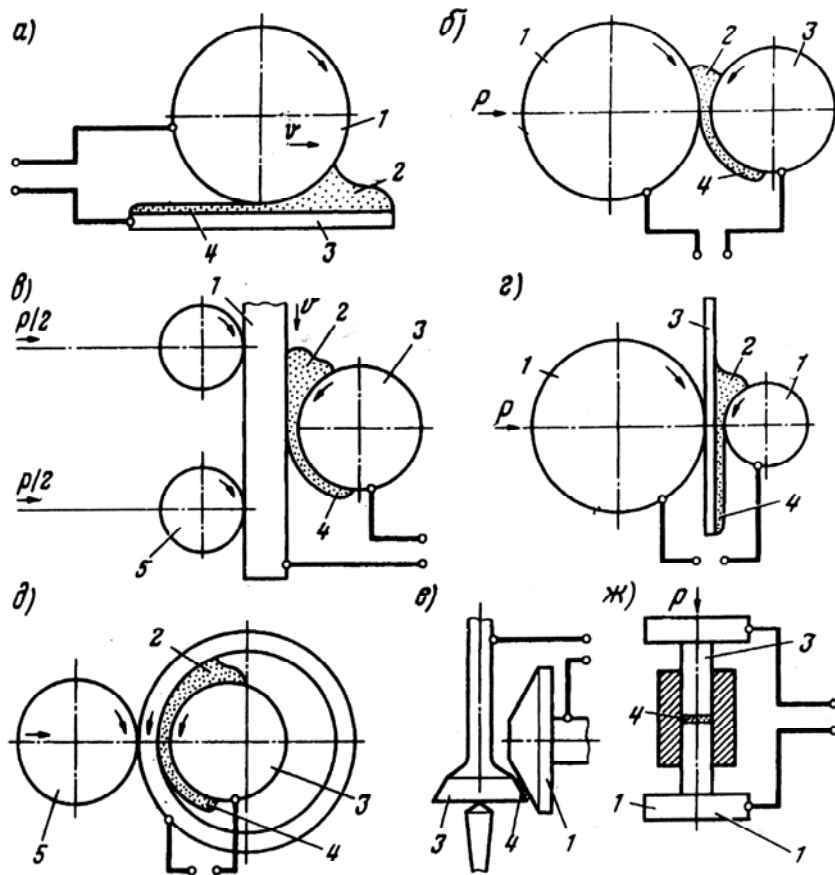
Схема электроконтактной приварки порошков на поверхности:
